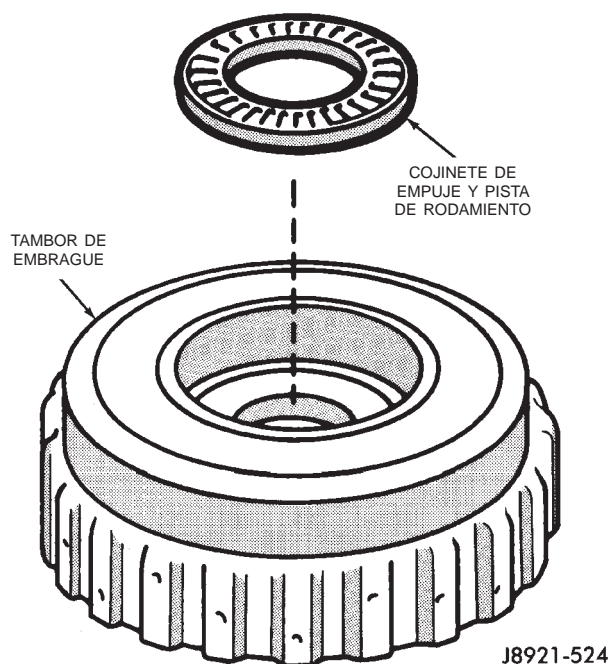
Desmontaje del cojinete y pista de rodamiento del tambor de embrague
